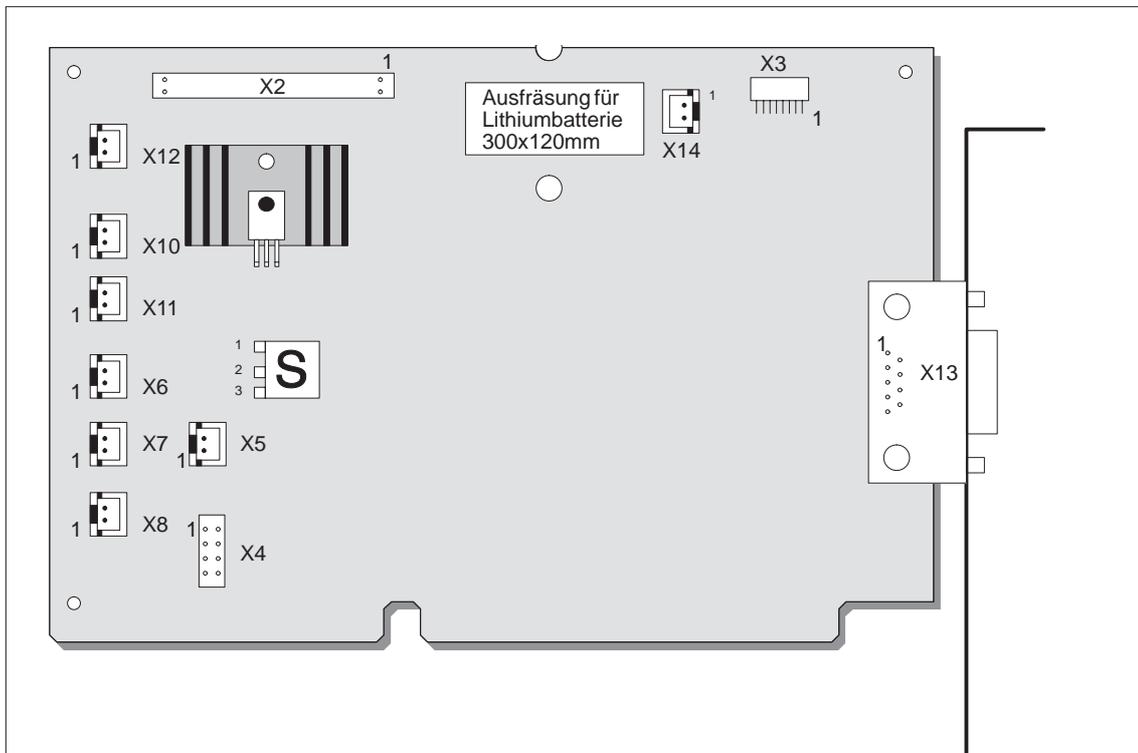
Lage der Stecker und Schalter auf der SafeCard
